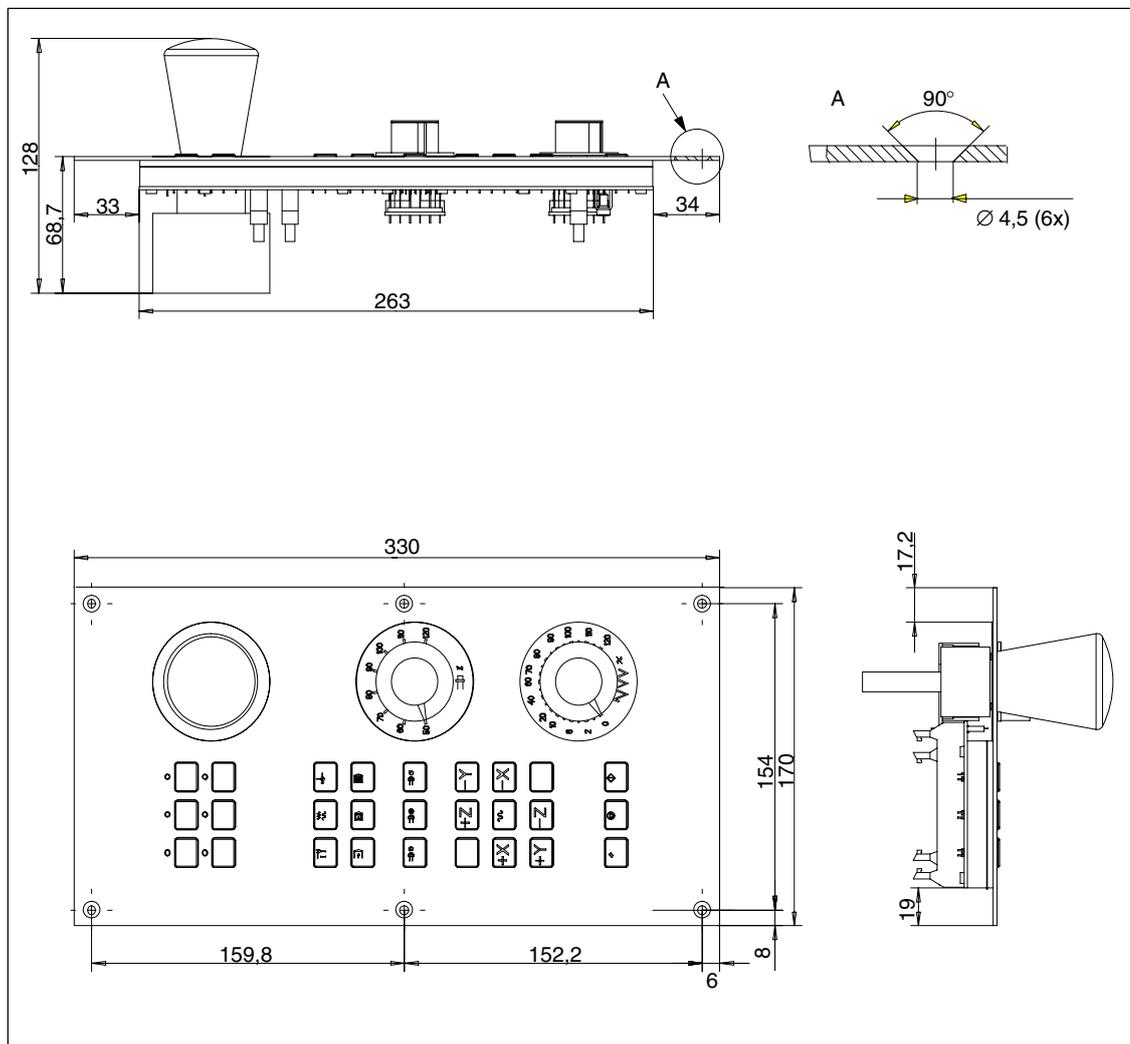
Disegno quotato della pulsantiera di macchina
